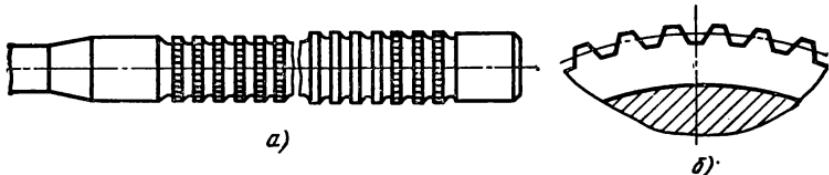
Протяжка для протягивания шлицев с треугольным профилем (елочная):
